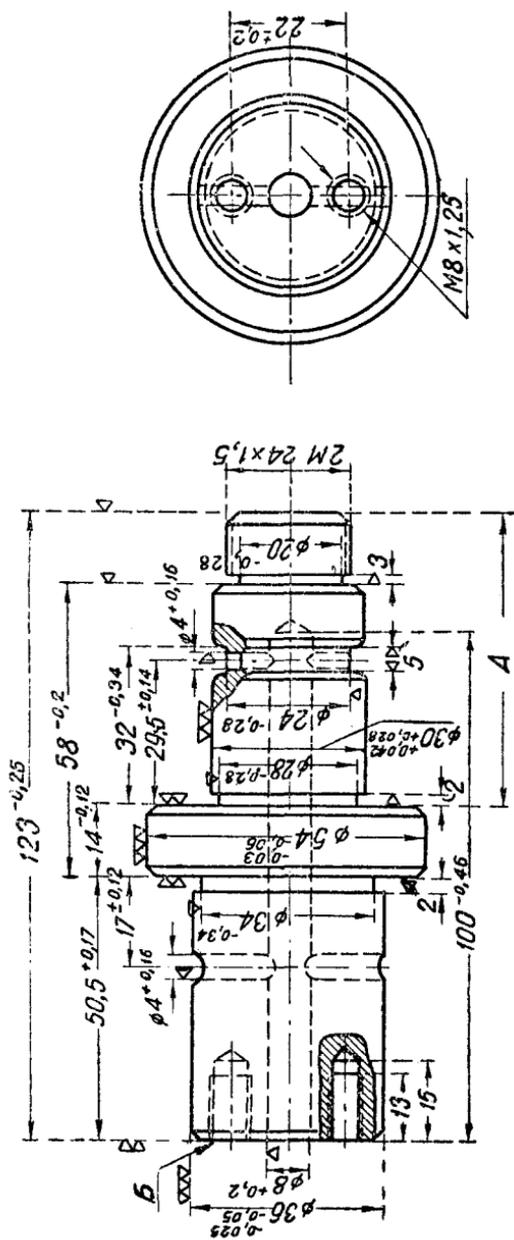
Дет. А03-4. Палец паразитной шестерни
